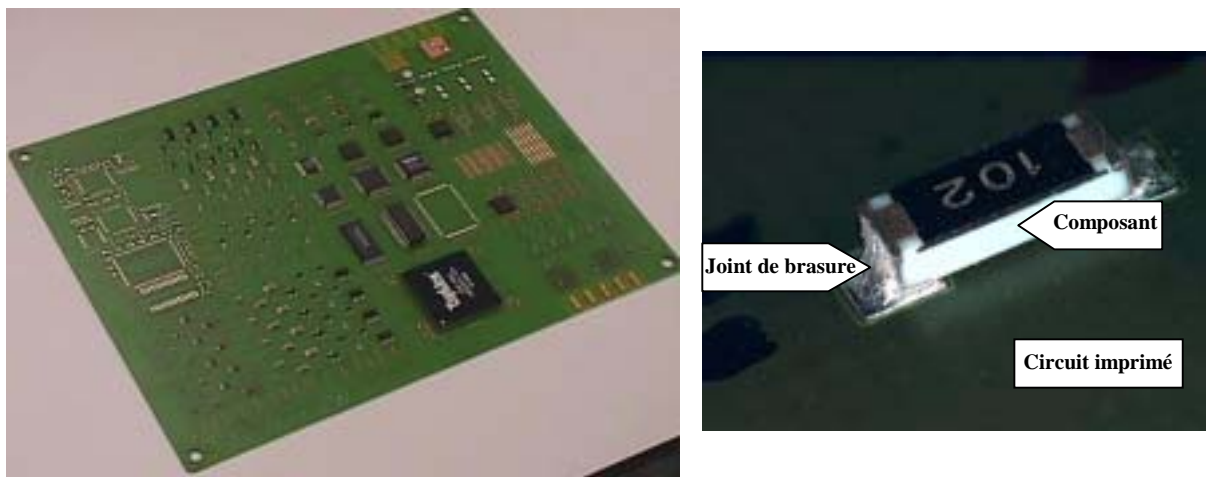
Assemblage électronique a) vue d'ensemble, b) vue d'un composant.
